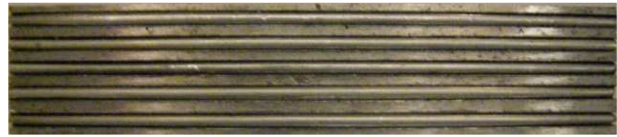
Заготовки, що мають подовжні пази з вставками з сталі Х18Н9Т
